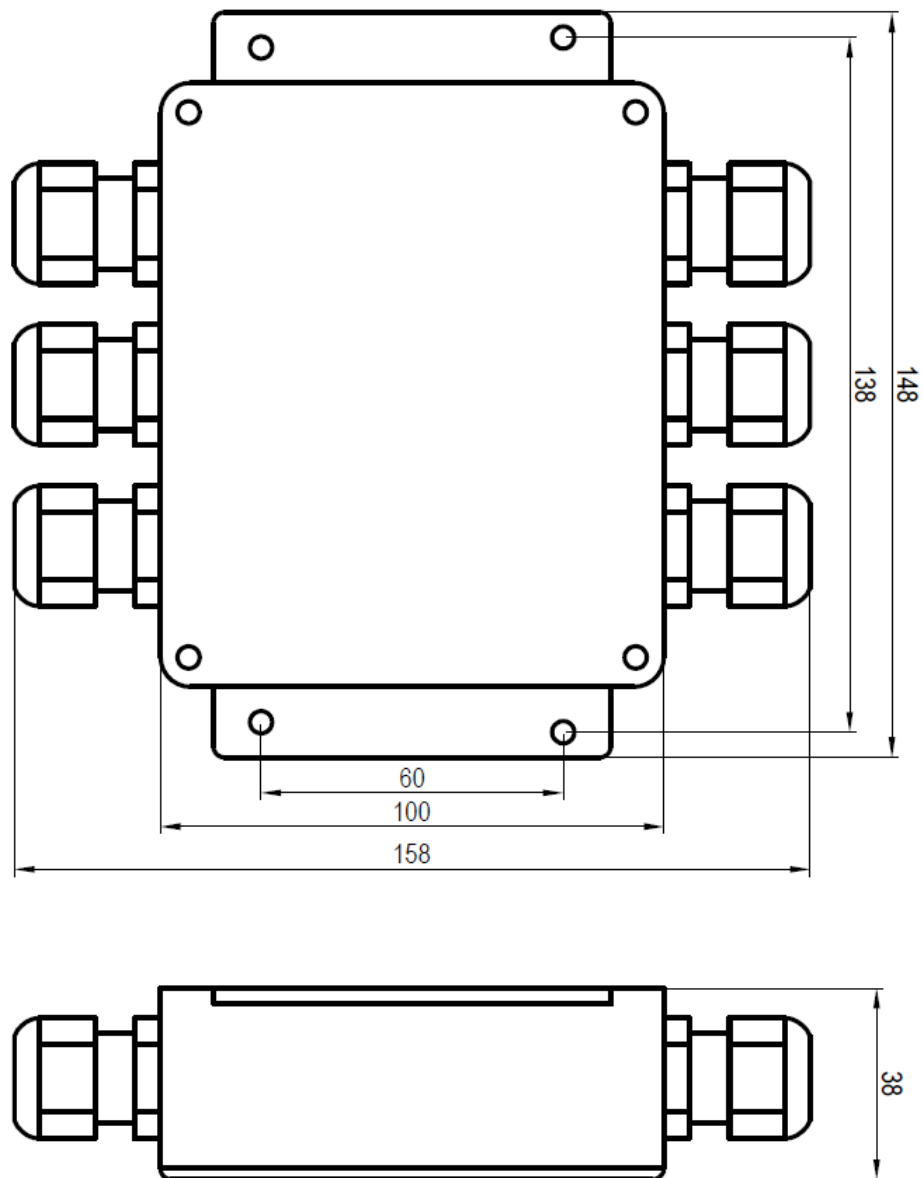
Габаритные и установочные размеры модуля Концентратор-КД1
